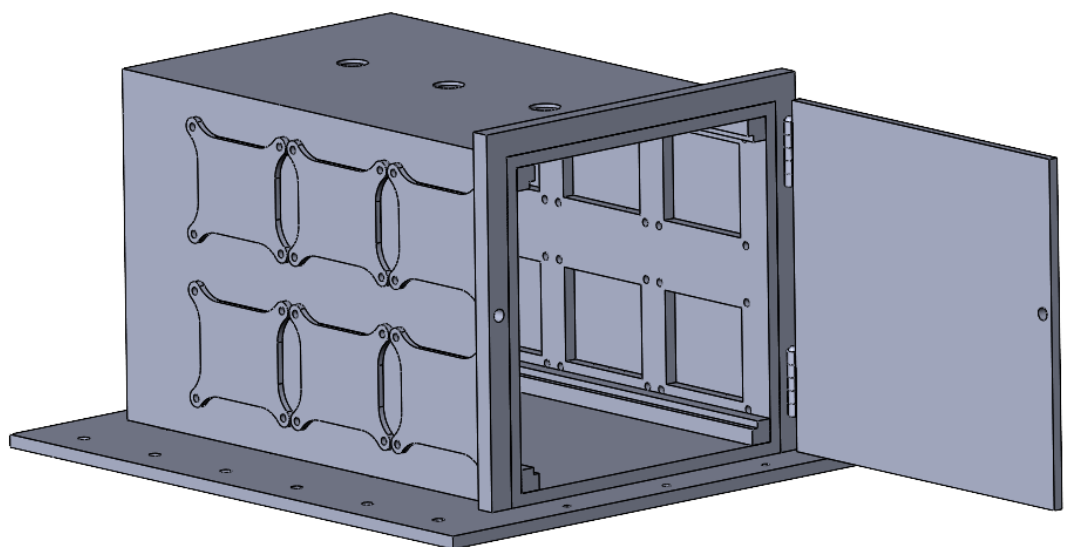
Модель ИТПК для порошкового металлического 3D принтера
